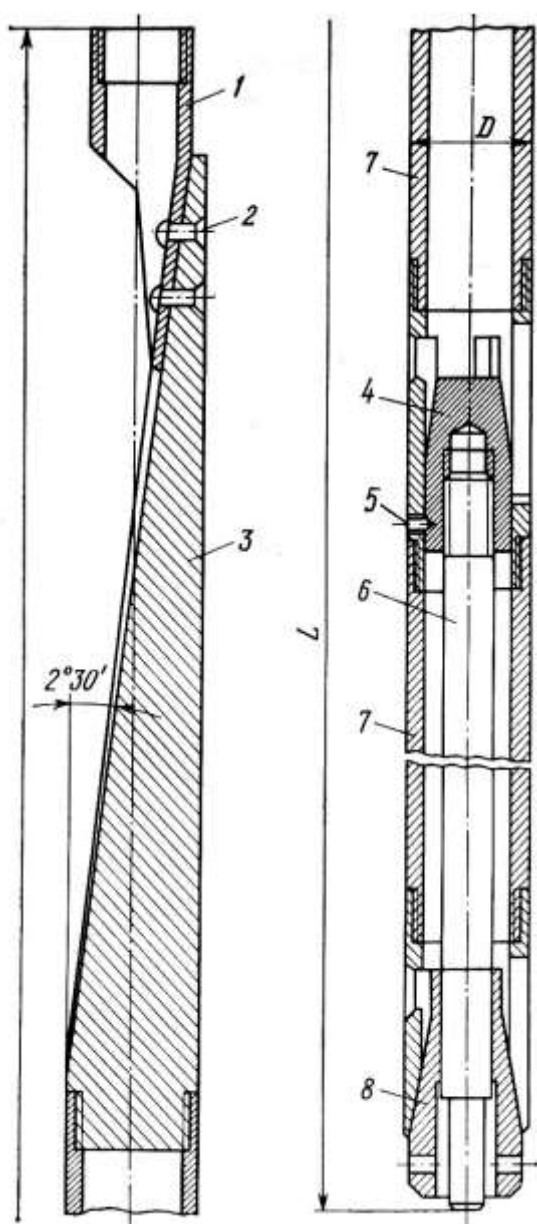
Стаціонарний відхиляючий клин КОС: 1 – установлювальна труба; 2 – заклепки; 3 – клин; 4, 8 – розпірні конуси; 5 – кріпильний гвинт; 6 – шток; 7 – з’єднувальний патрубок
